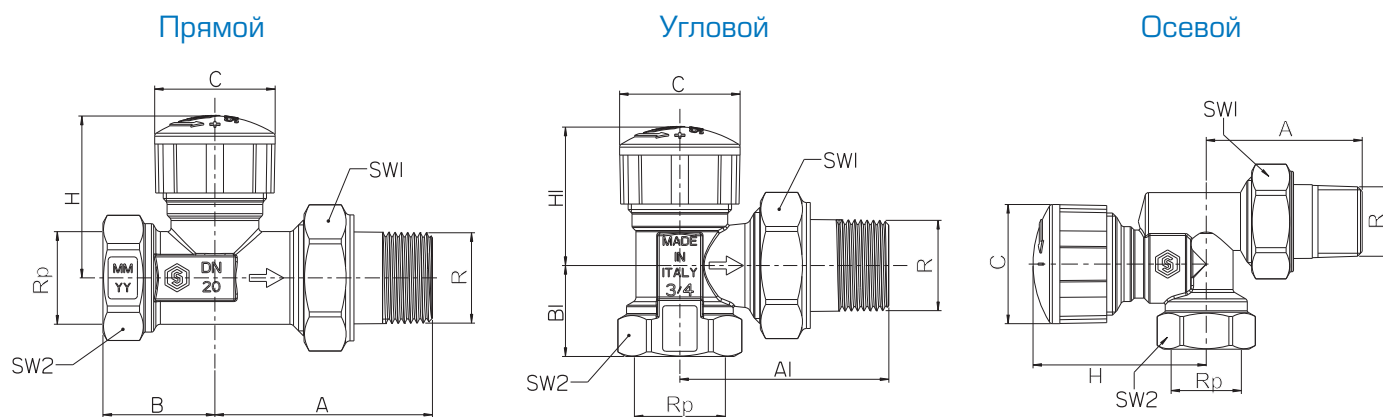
Габаритные и присоединительные размеры терморегулирующего клапана STOUT
